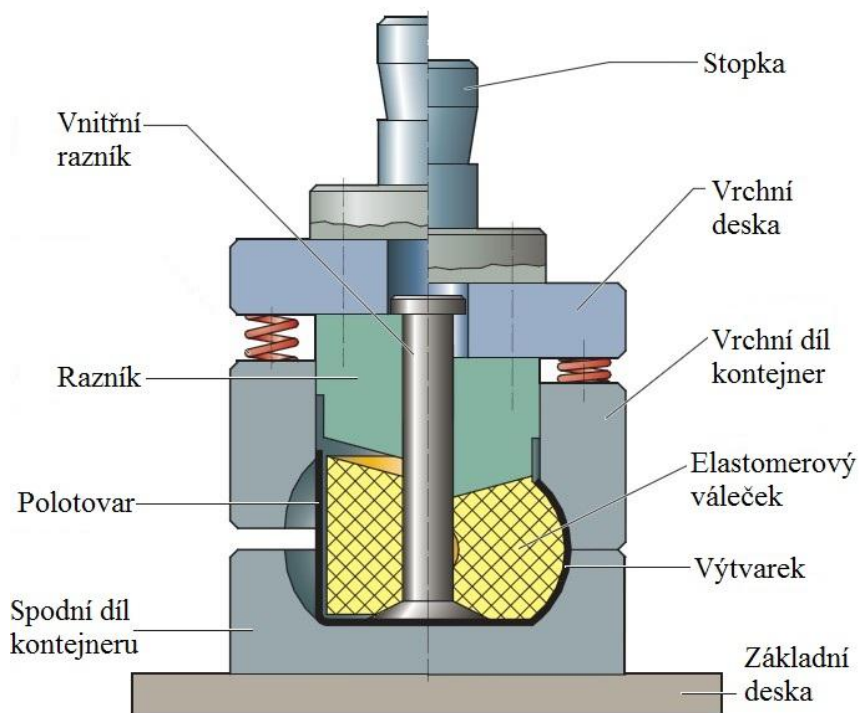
Příklad výtvaru tvářeného radiálním vypínáním [5]
